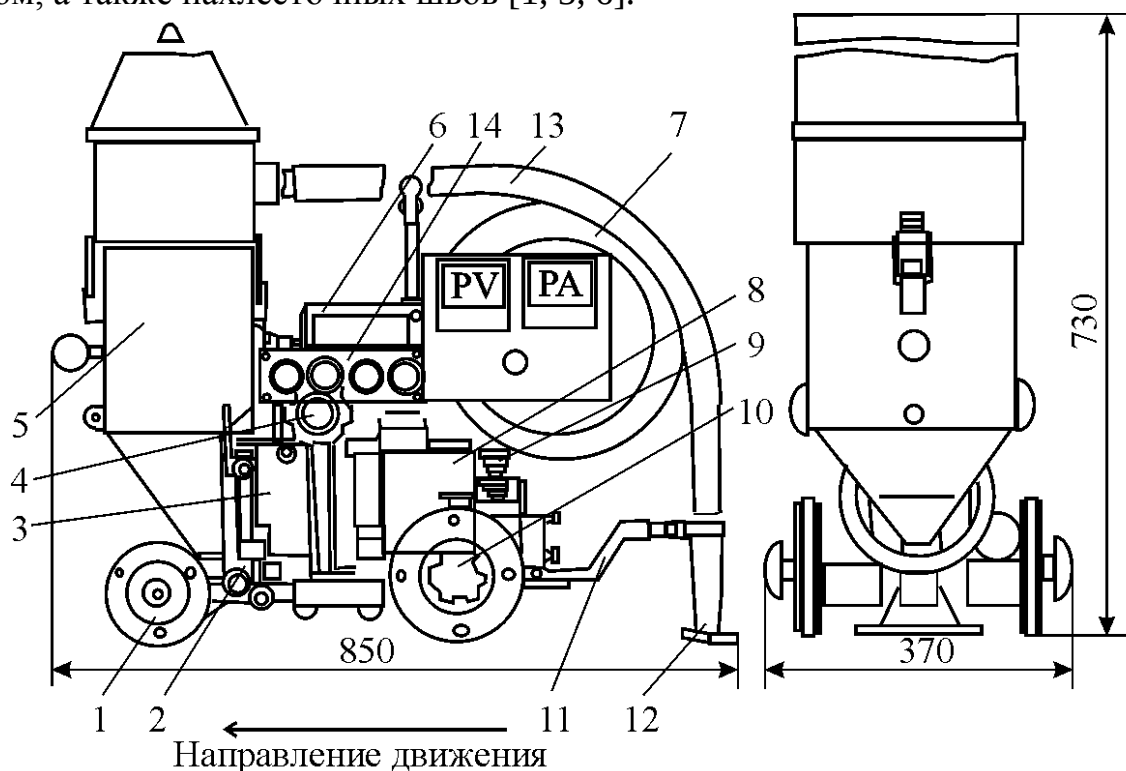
Общий вид сварочного автомата АДФ-1002: 1 – переднее шасси; 2 – токоподвод; 3 – сварочная головка; 4 – корректировочный механизм; 5 – бункер для флюса; 6 – кронштейн; 7 – кассета; 8 – двигатель; 9 – ходовой механизм; 10 – маховичок; 11 – кронштейн; 12 – сопло; 13 – шланг; 14 – пульт управления
